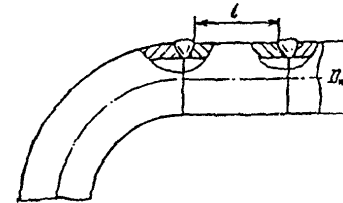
Расположение сварных швов при приварке колена к трубе
